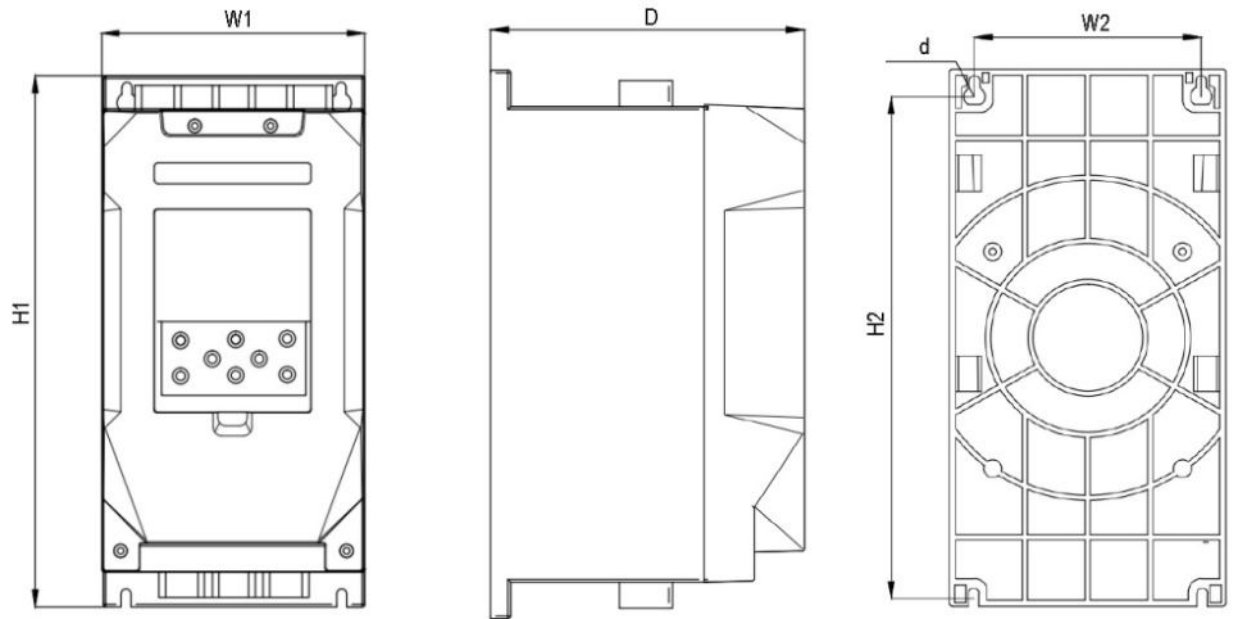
Габаритные и установочные размеры RR1
